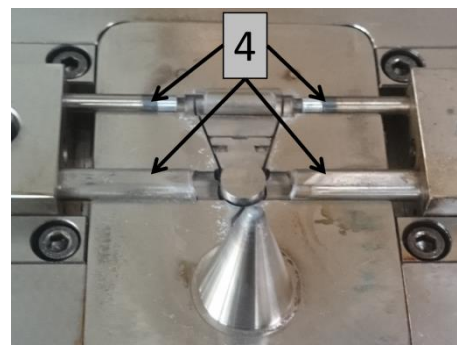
Druckgusswerkzeug (Auswerferseite) für Verstärkungseinleger aus Zink
